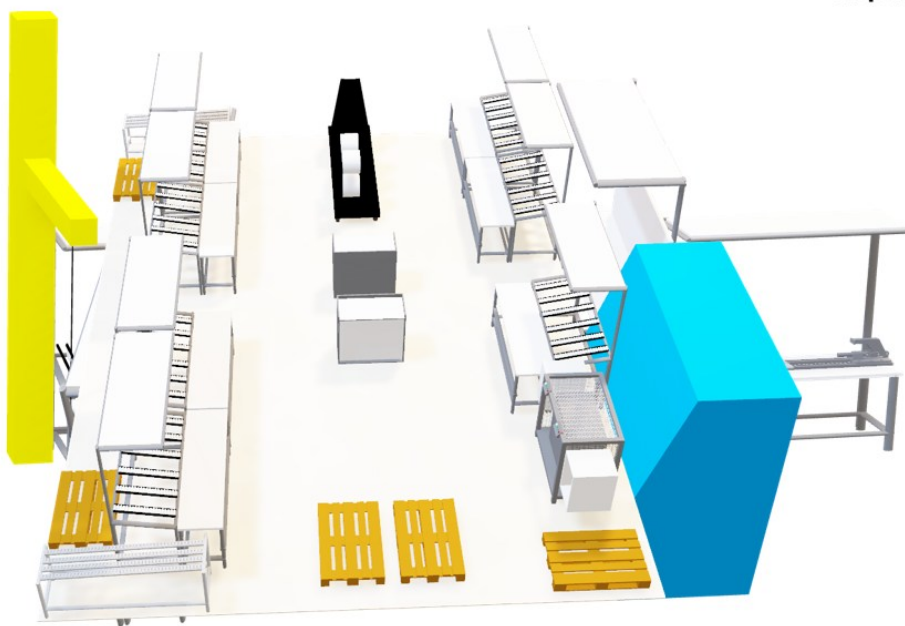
Vista tridimensionale della postazione accorpata di premontaggio
